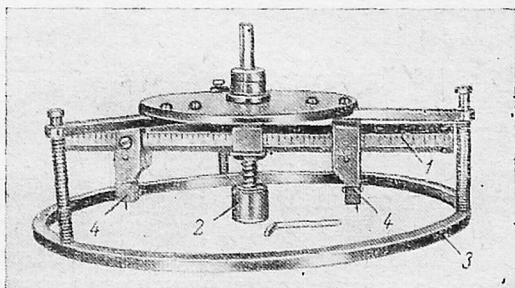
Приспособление для вырезания резиновых уплотнителей из листа.
